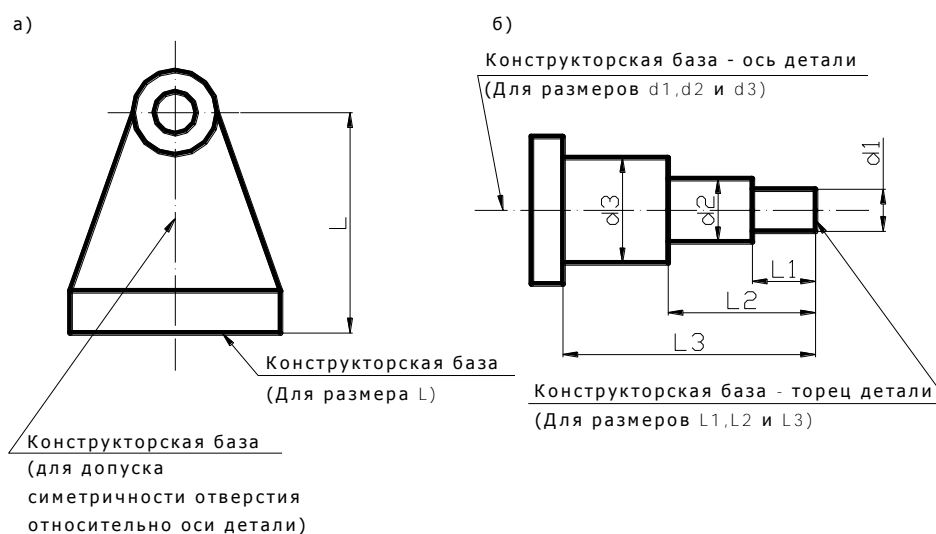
Примеры определения положения конструкторских баз для обрабатываемого сквозного отверстия (а) и ступенчатого вала (б).
